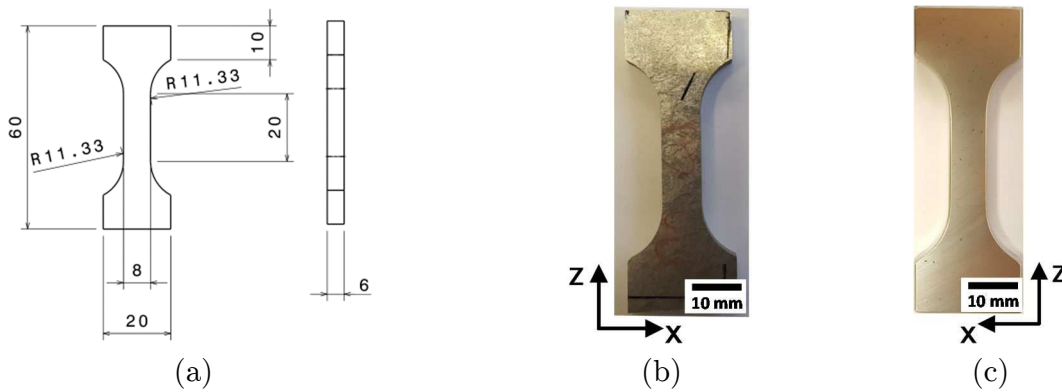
(a) Plan de l'éprouvette plate à prélever sur la surface du carter de transmission, (b) éprouvette prélevée par électroérosion (face avec état brut de fabrication), (c) face arrière de l'éprouvette après polissage
